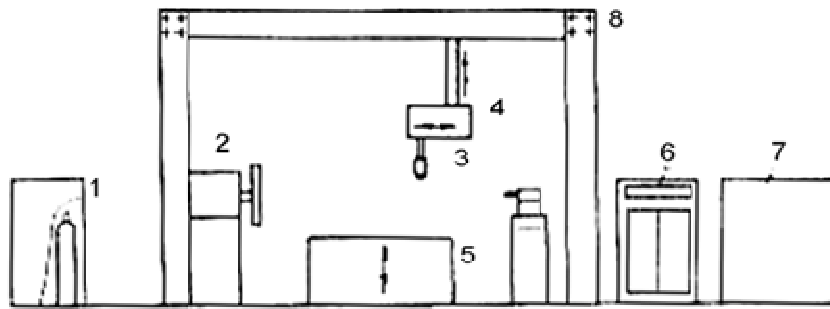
Общий вид плазменного технологического комплекса: 1- блок газового обеспечения; 2-вращатель; 3-плазматрон; 4-механизм перемещения плазматрона; 5-стол; 6-источник питания; 7-блок водяного обеспечения; 8-кабельшланговый пакет
